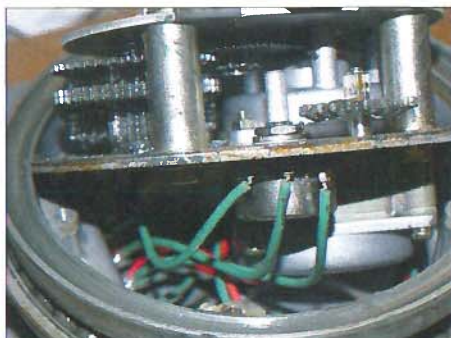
Montageplatte mit Getriebe und Potenziometer; das Zahnrad auf dessen Achse wurde zuvor entfernt.
